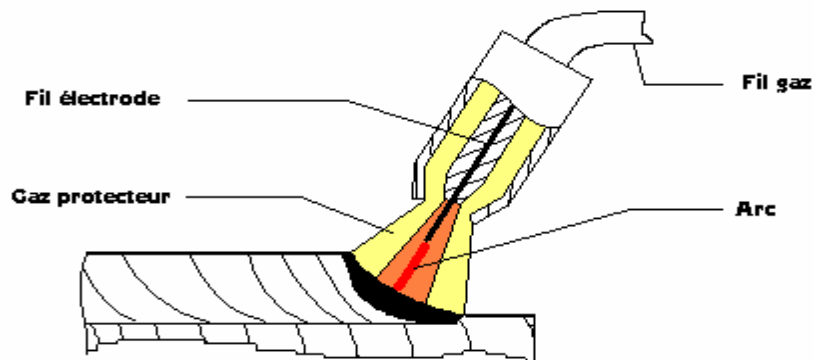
Principe des soudages MIG et MAG [7].
